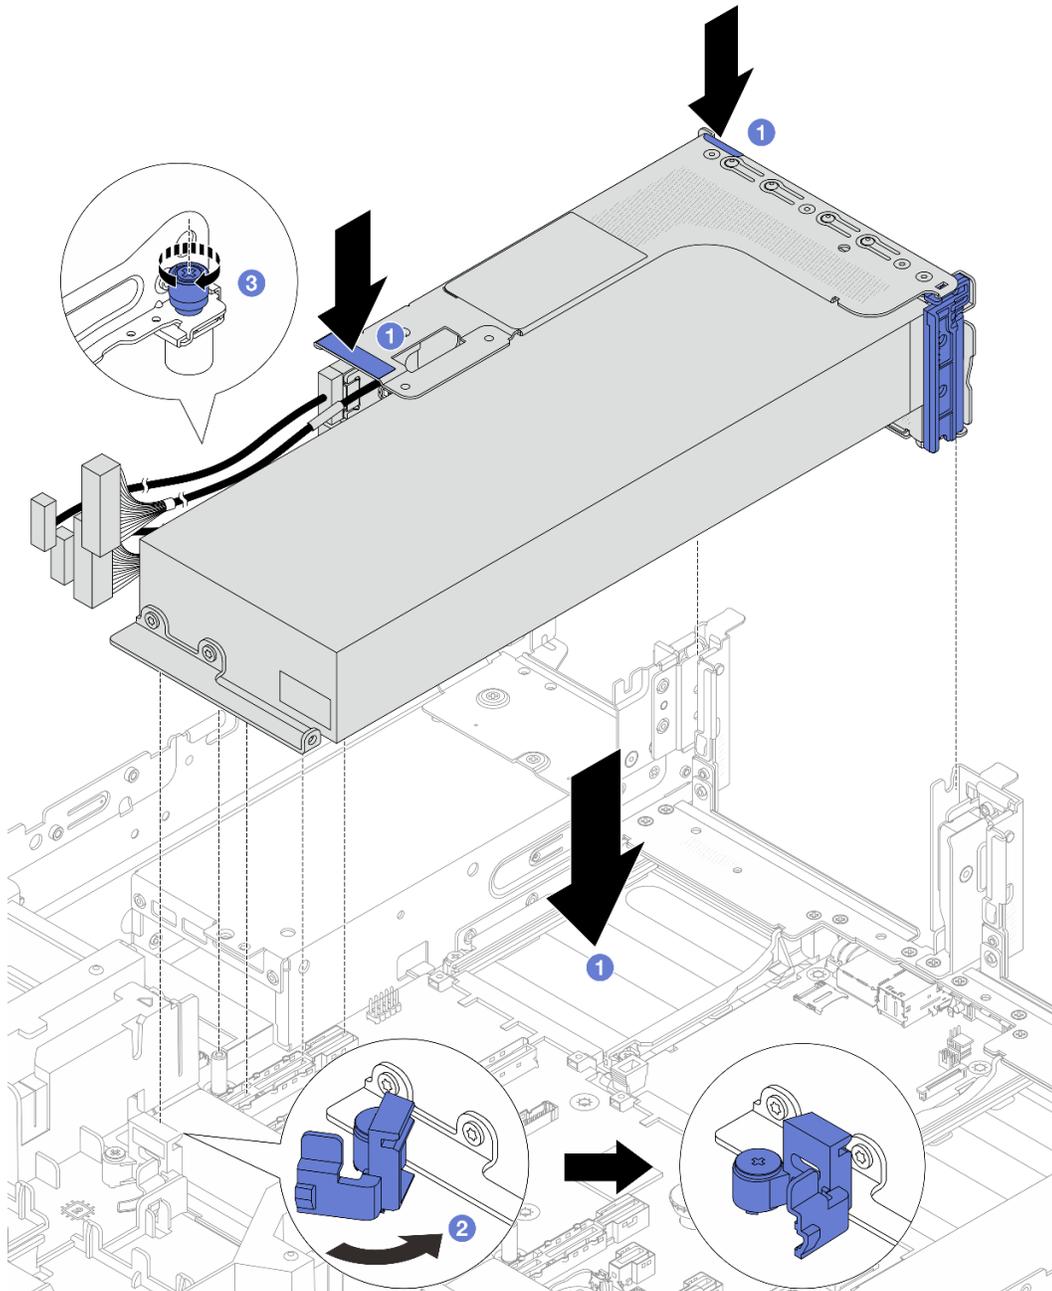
Instalação do conjunto de placa riser com o adaptador GPU
